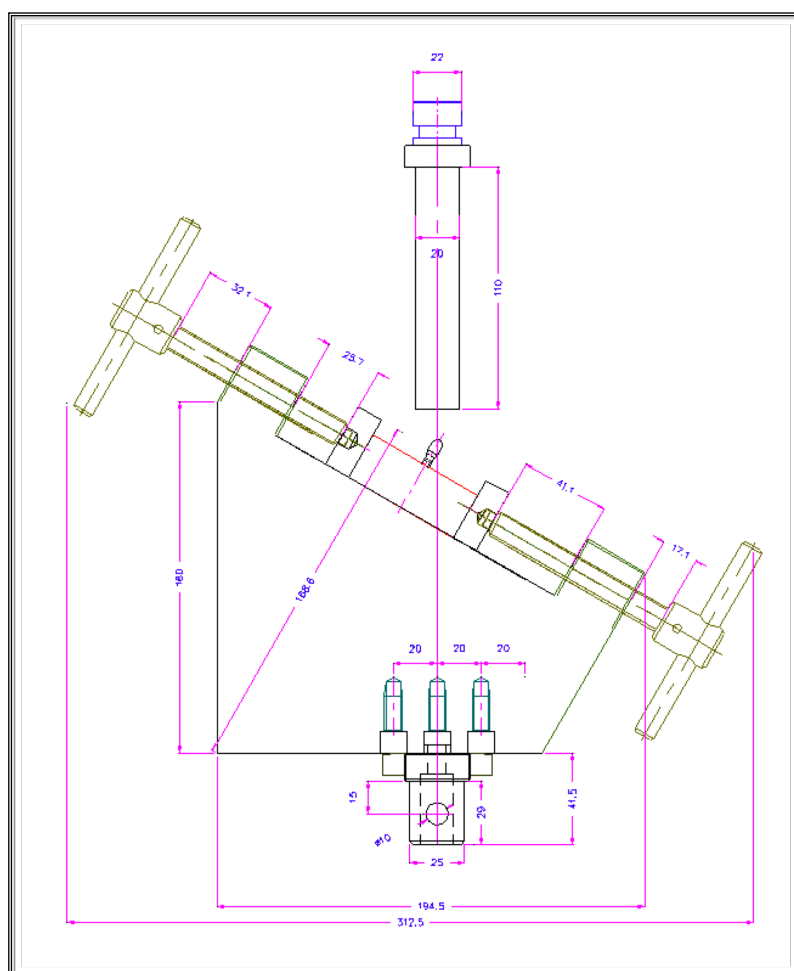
Plano de la pieza utilizada para la colocación de las muestras en un ángulo de 30°.
